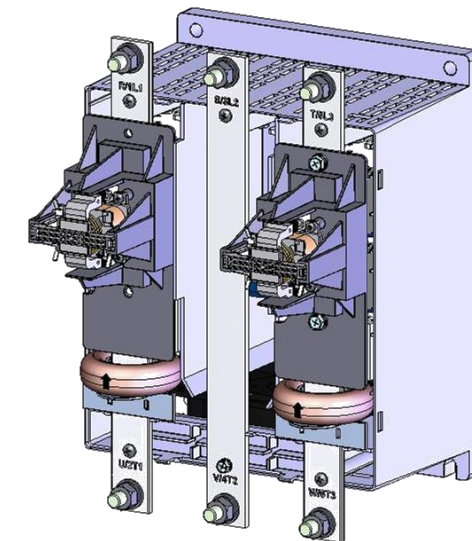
Зовнішній вигляд силової частини пристрою плавного пуску із обхідними контакторами
